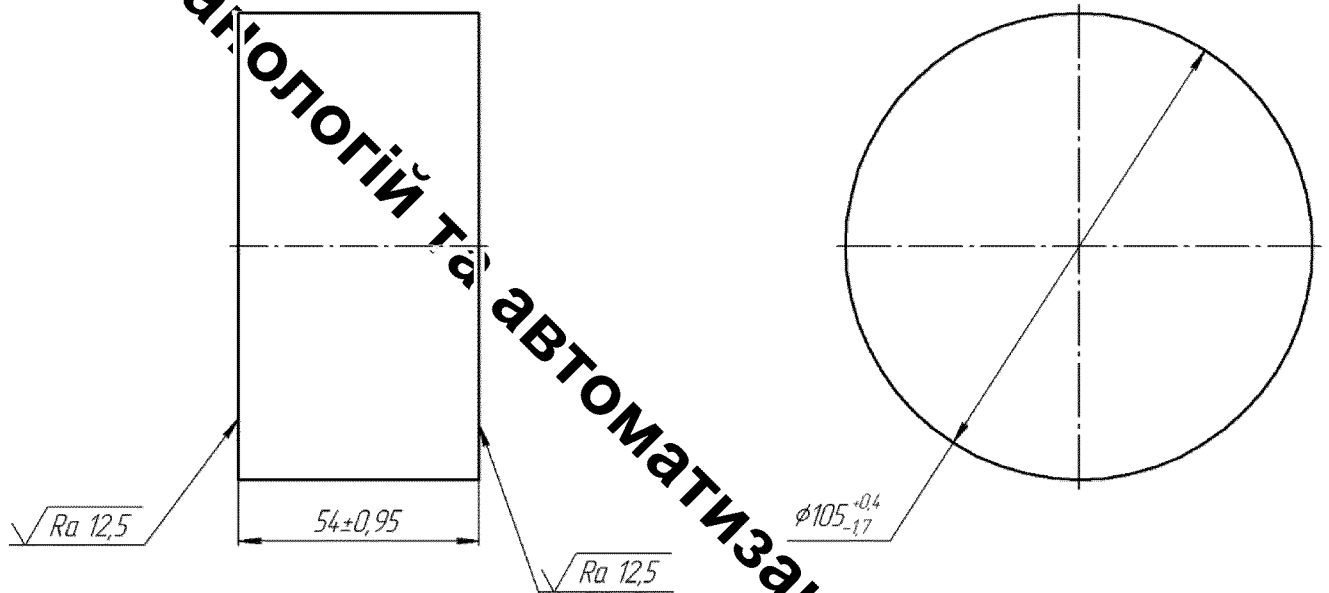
Заготовка деталі «Корпус Д02120.1» із штучного круглого сортового прокату
